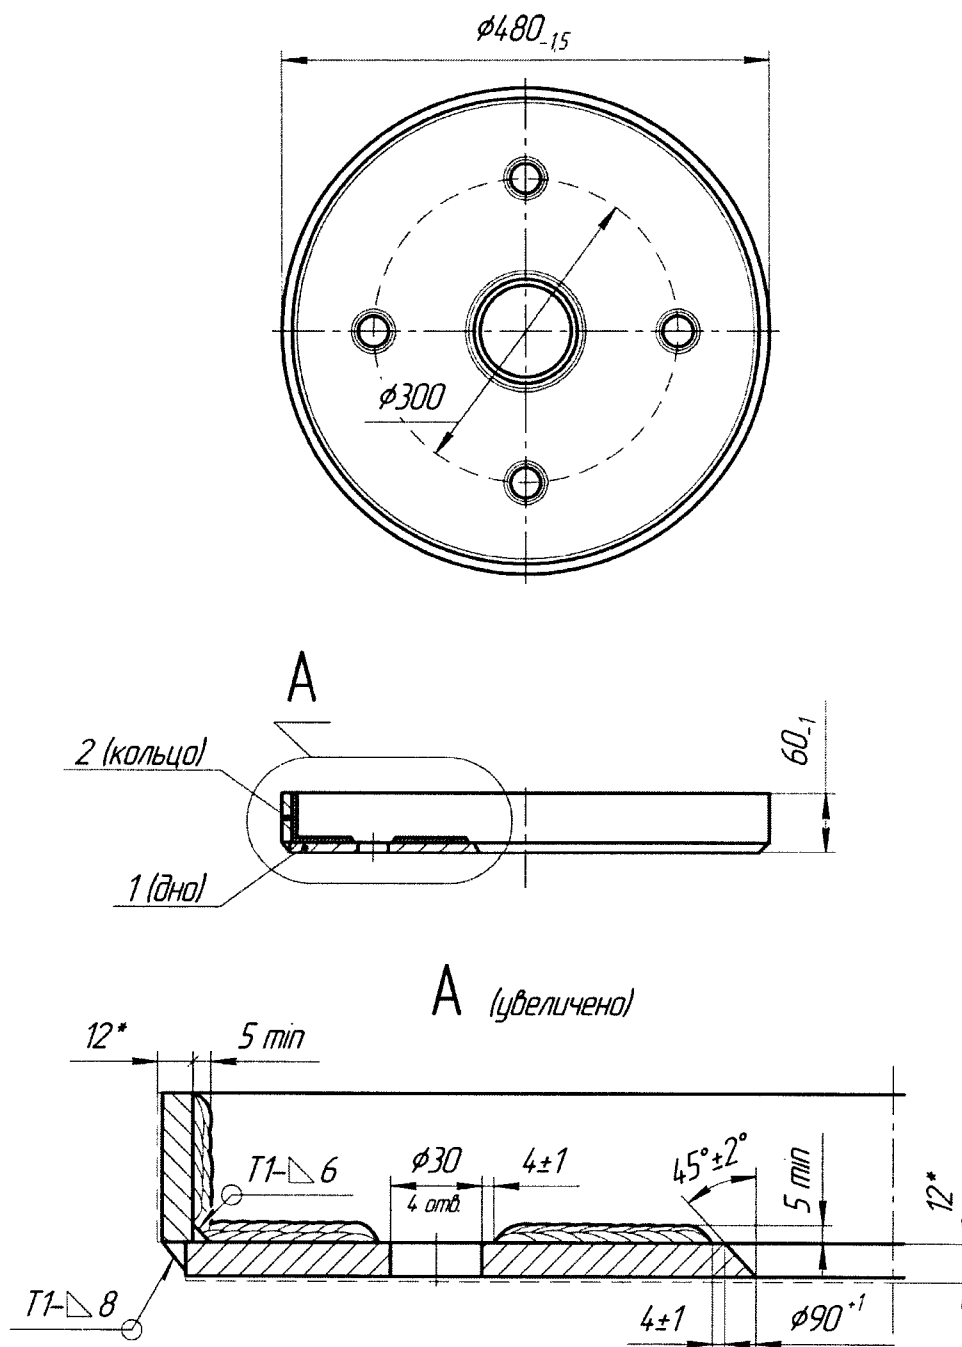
Вставка подпятника с износостойкой наплавкой (сварной вариант)
